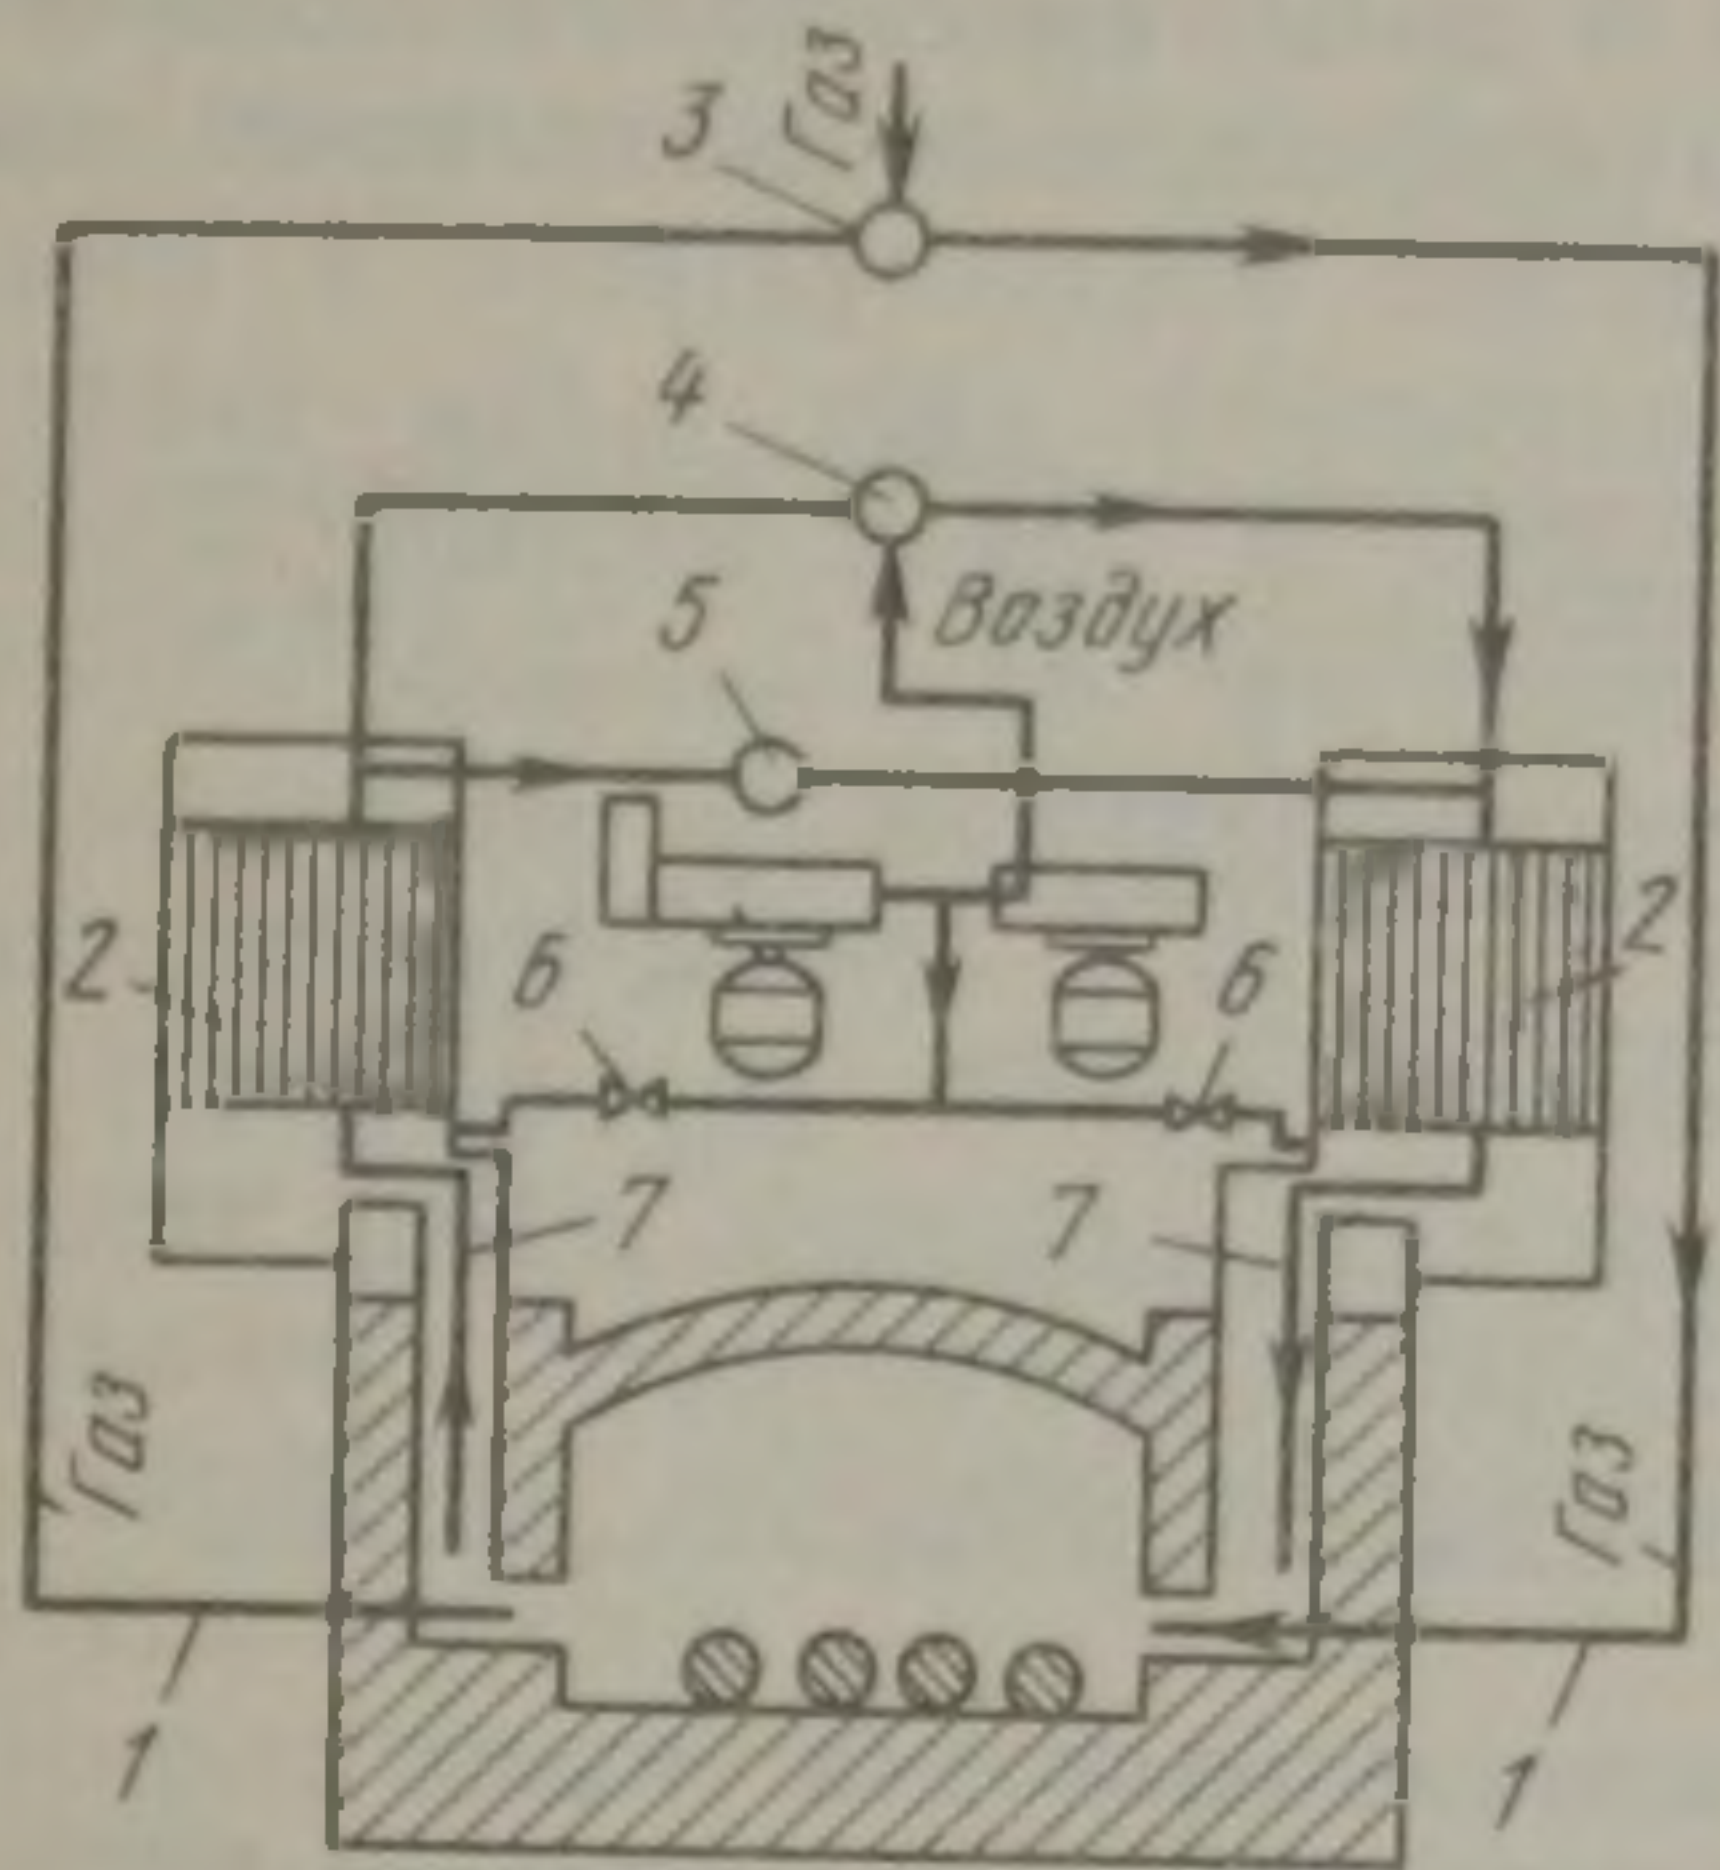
Схема печи малоокислительного нагрева металла с металлическими регенераторами:
